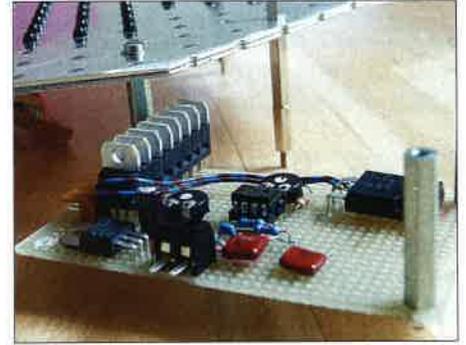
Die Ansteuerelektronik wurde auf eine Universallochrasterplatte aufgebaut und über Abstandsbolzen hinter der Lochbleche befestigt. Fotos: DH6TF
